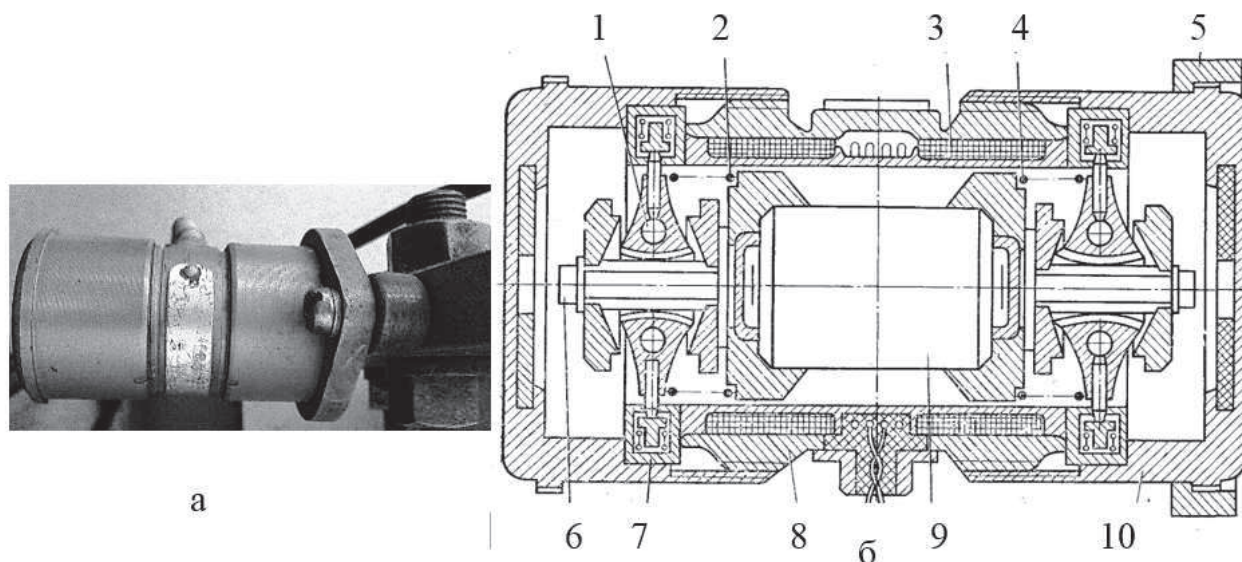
Внешний вид (а) и конструктивная схема (б) датчика вибрации МВ-25 (1–сектор; 2,4–пружина; 3–катушка; 5–фланец; 6–крышка; 7–постоянный магнит; 8–корпус; 9–подшипник; 10–винт [6])
